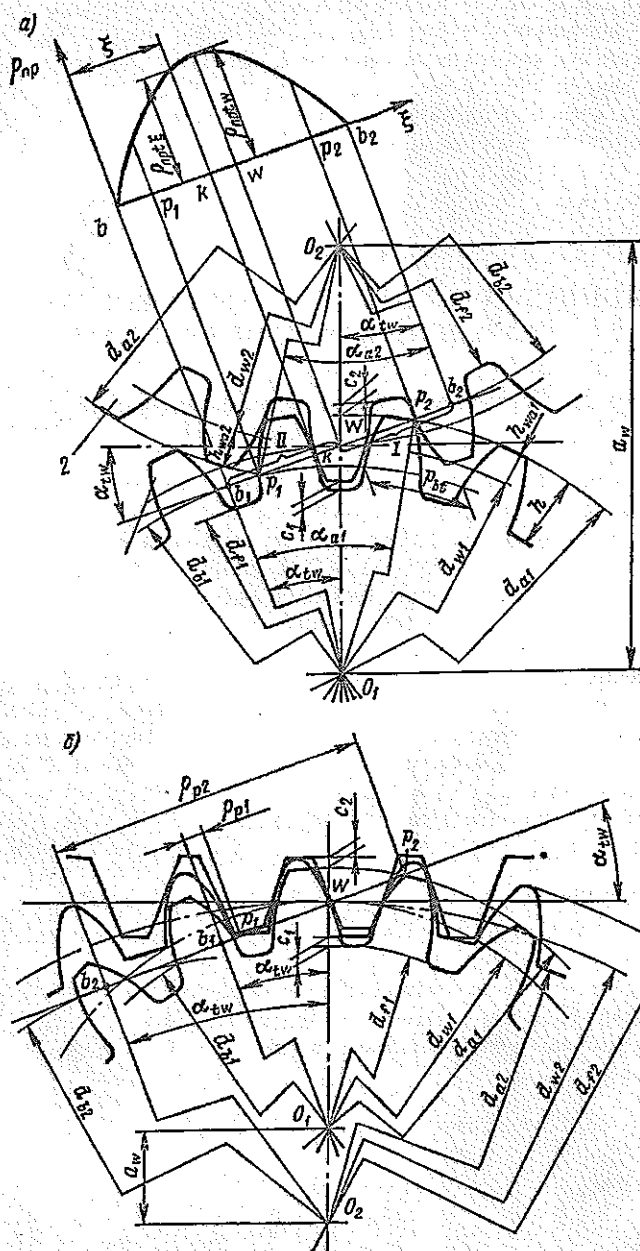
Зацепление эвольвентной цилиндрической передачи:
